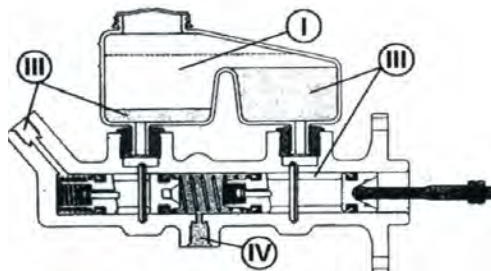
Положение деталей главного тормозного цилиндра с центральными поршневыми клапанами при возникновении неисправности в одном из контуров
